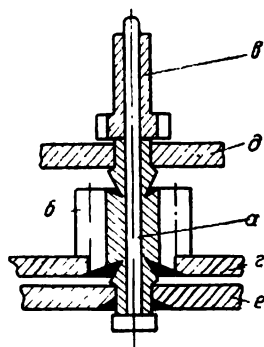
Стержень минутной стрелки: а — стержень минутной стрелки; б — триб центрального колеса; в — минутный триб; г — центральное колесо; д — платина; е — мост центрального колеса
